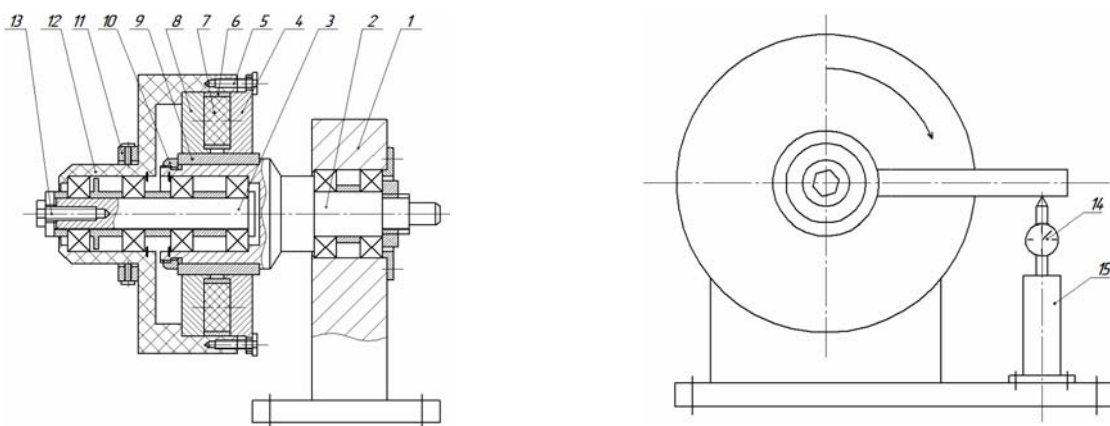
Схема экспериментальной установки: 1 – стойка; 2 – подвижный вал; 3 – неподвижный вал; 4 – съемный полюс; 5 – болт; 6 – диск; 7 – магнит; 8 – съемный полюс; 9 – сменная втулка; 10 – гайка; 11 – хомут; 12 – корпус; 13 – болт; 14 – индикатор; 15 – опора
